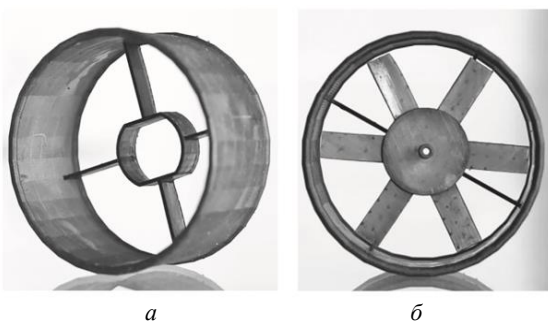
Макет подруливающего устройства: а – корпус; б – макет в сборе
